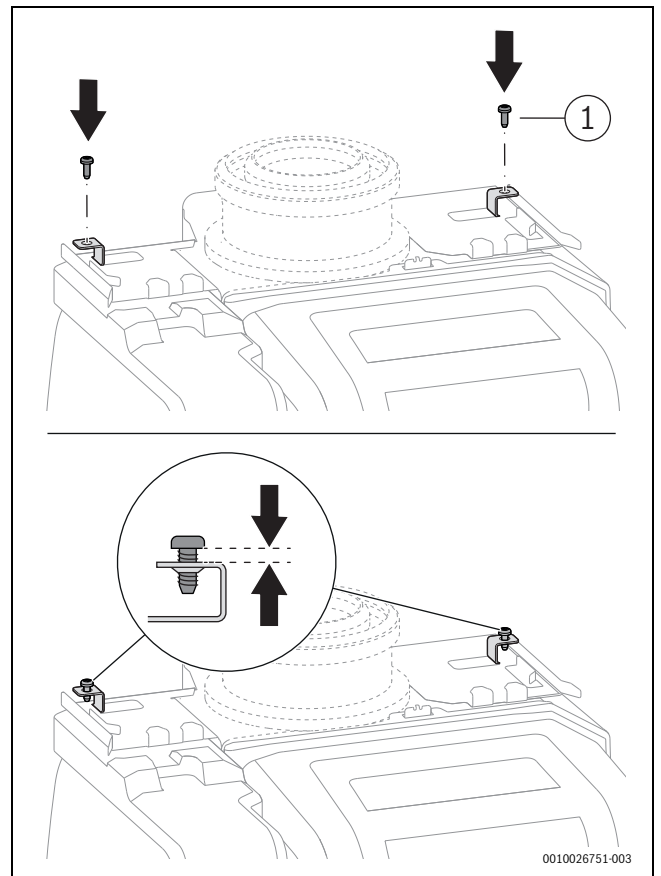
Schrauben für die Oberseite der Geräteverkleidung locker eindrehen
